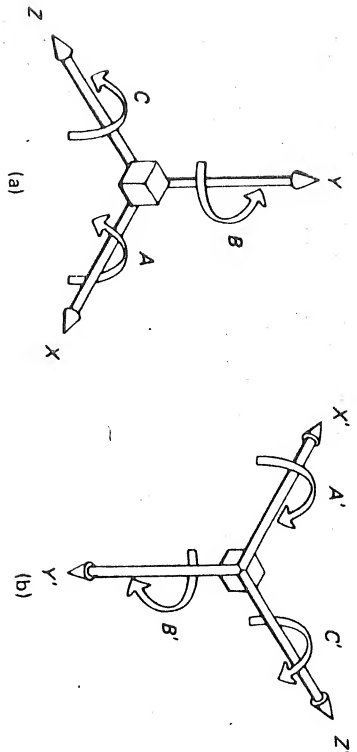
Sistema de coordenadas para la especificación de los movimientos de una máquina herramienta. (a) Movimientos de la herramienta; (b) movimientos de la pieza.
